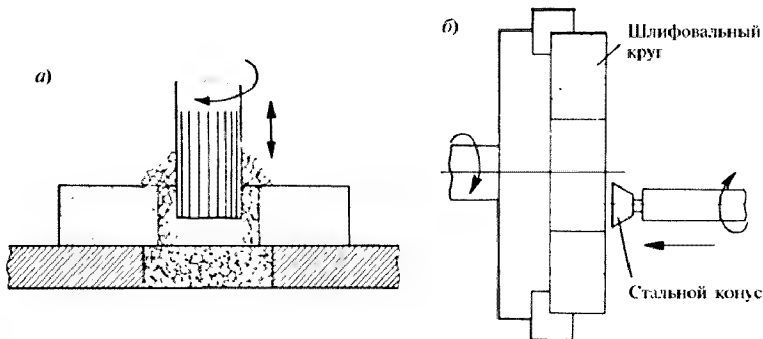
Схема обработки отверстия в круге на сверлильном станке специальным сверлом, чугуном, стальным или абразивным зерном (а) и на токарных станках стальными конусами (б)
